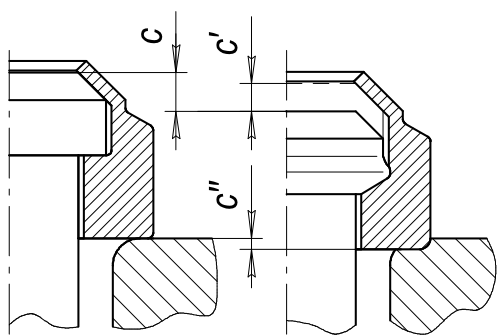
Зміна форми головки штока і стопорної шайби в процесі напрацювання ресурсу клапана
